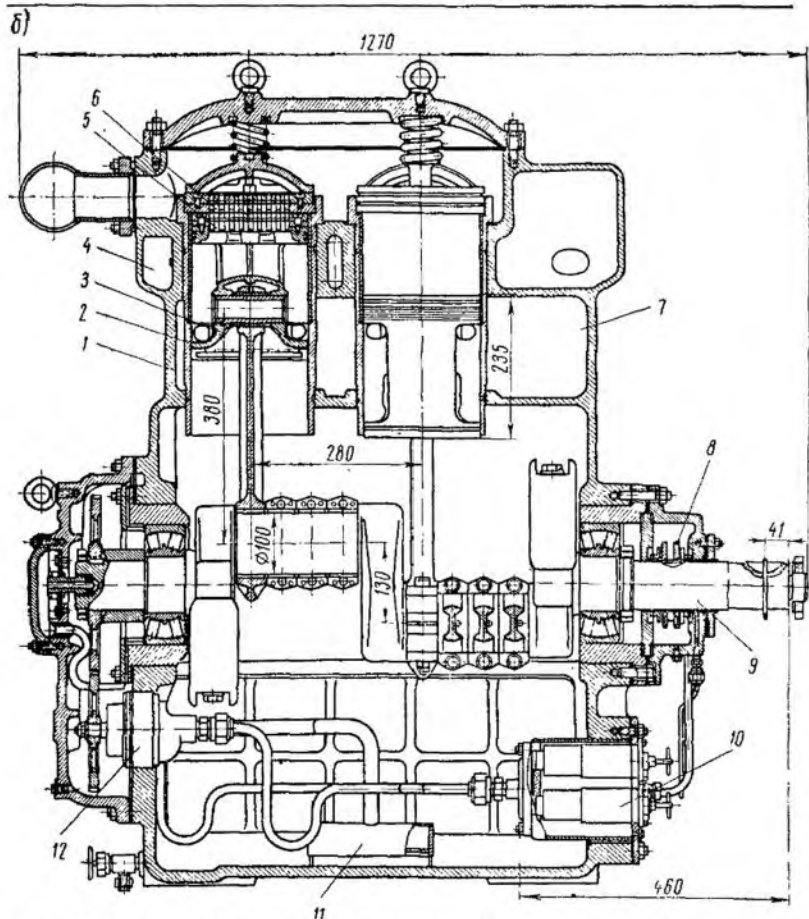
Блоккартерные восьмицилиндровые компрессоры:
